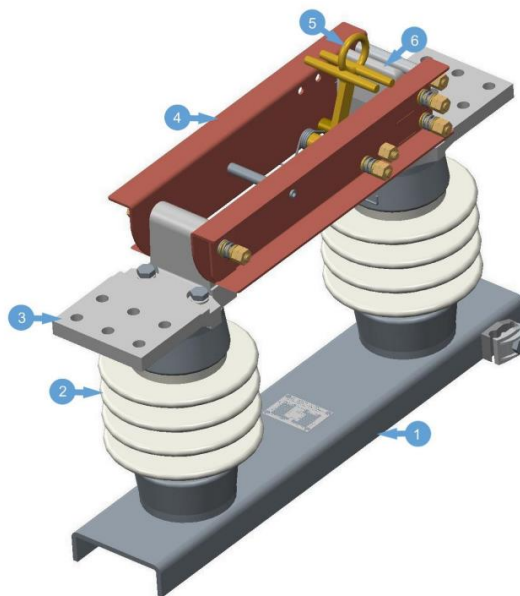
Chaves seccionadoras tipo faca (FC) até 36,2 kV
